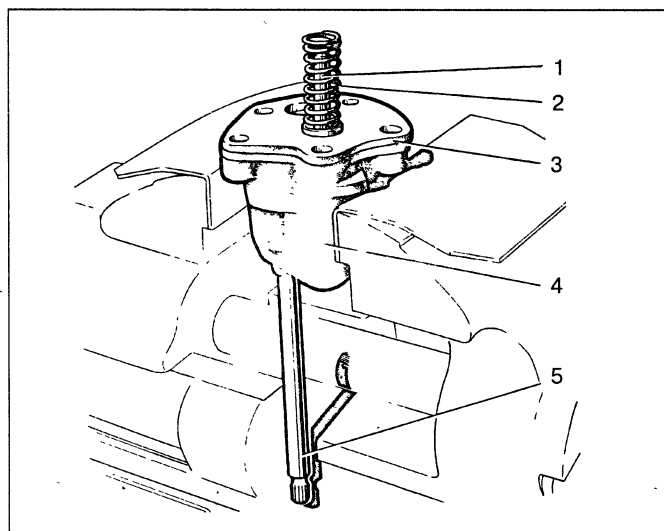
Разборка масляного насоса: 1 – редукционный клапан; 2 – пружина клапана; 3 – крышка; 4 – корпус; 5 – валик
